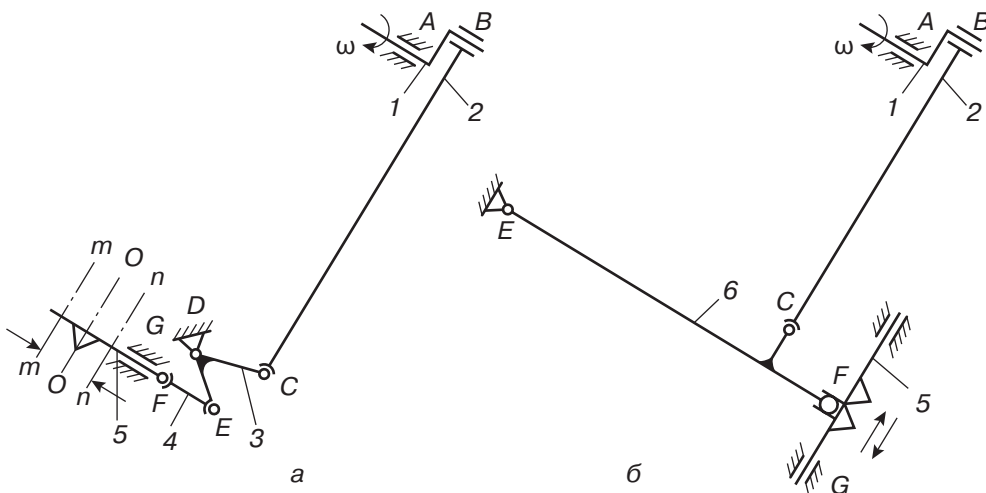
Схеми кривошипно-шатунних механізмів приводу ножа:
